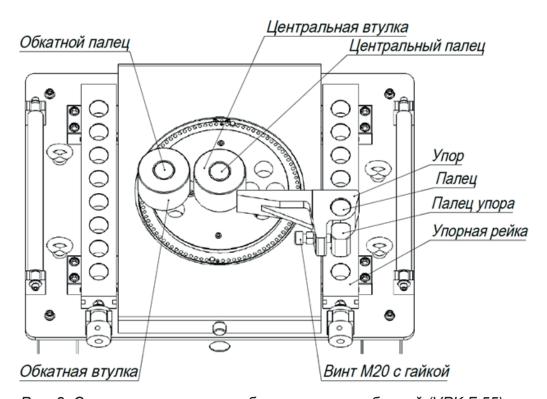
Схема расположения гибочных приспособлений (VPK Г-55)
